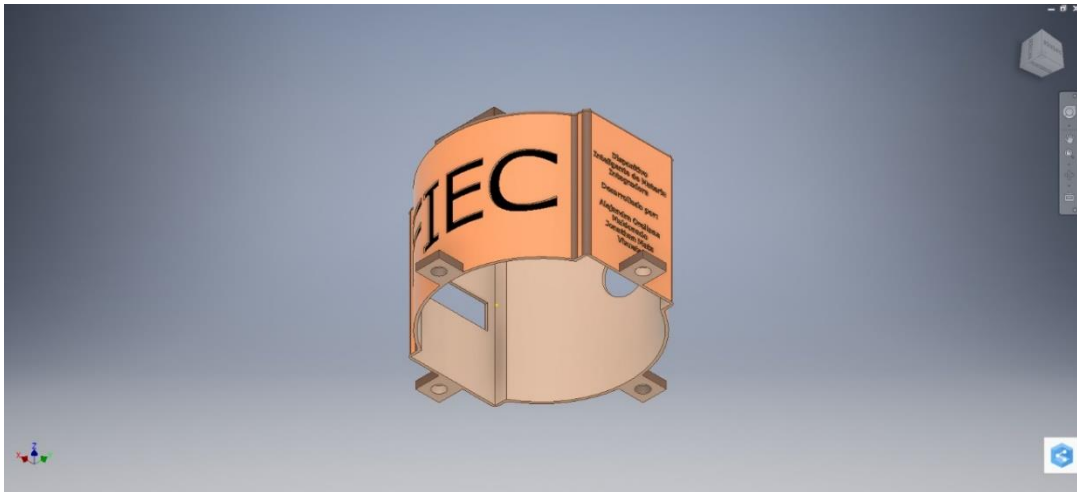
Modelo 3D de la estructura completa-vista 1
